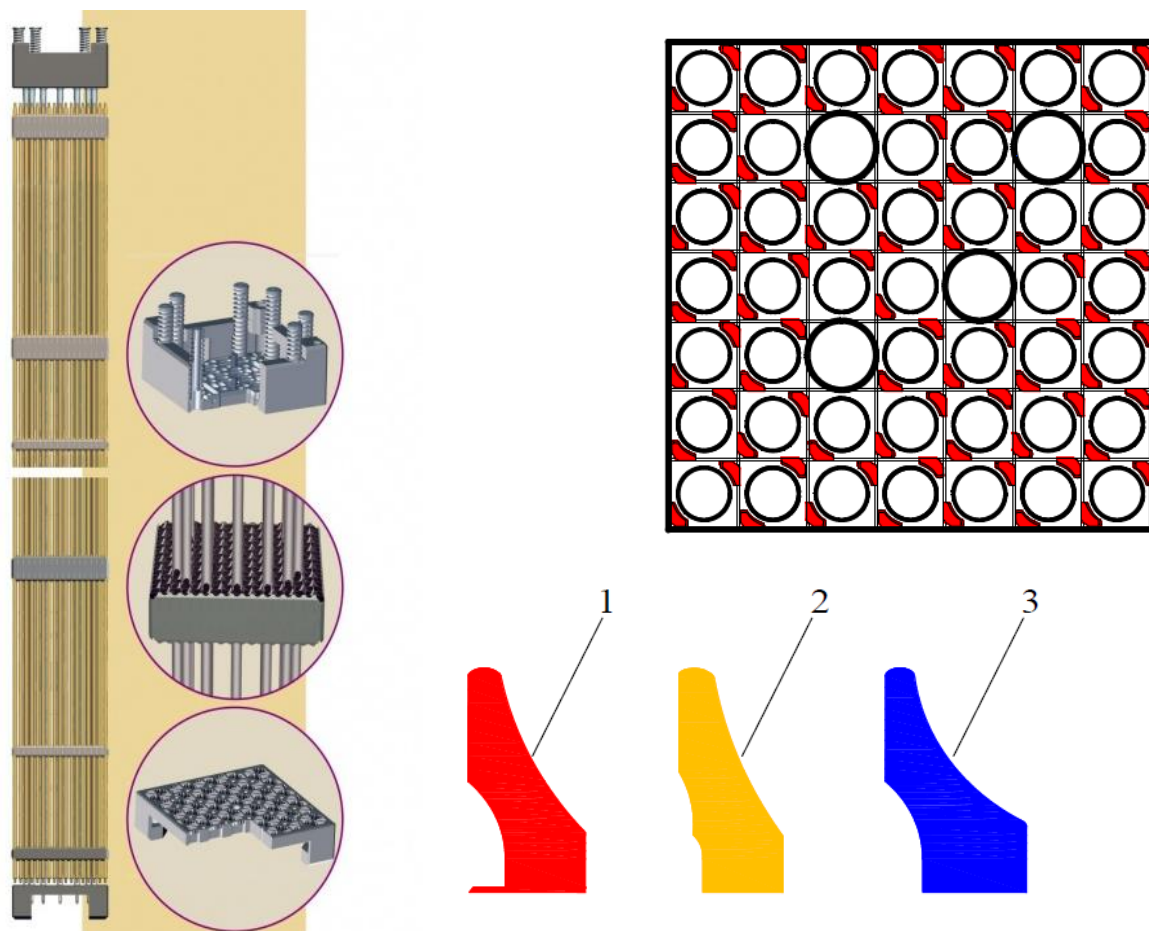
Конструкция ТВС-КВАДРАТ (слева) российского производства, конструкция перемешивающей дистанционирующей решетки (справа сверху), тип диффлектора перемешивающей решетки (справа внизу):
